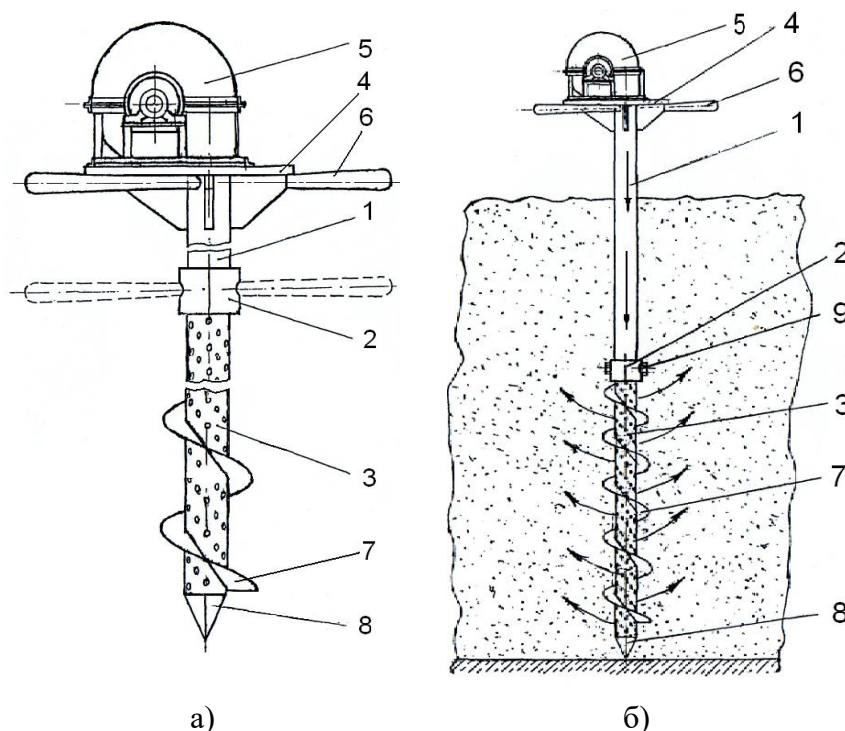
Модернізований переносний пристрій для активного вентилявання зерна; а) – будова; б) – пристрій у зерновому насипу: 1 – магістральний трубопровід; 2 – муфта; 3 – вентиляційна труба; 4 – платформа; 5 – вентилятор; 6 – ручка; 7 – гвинтова поверхня; 8 – кінцевик; 9 – гвинт стопорний
